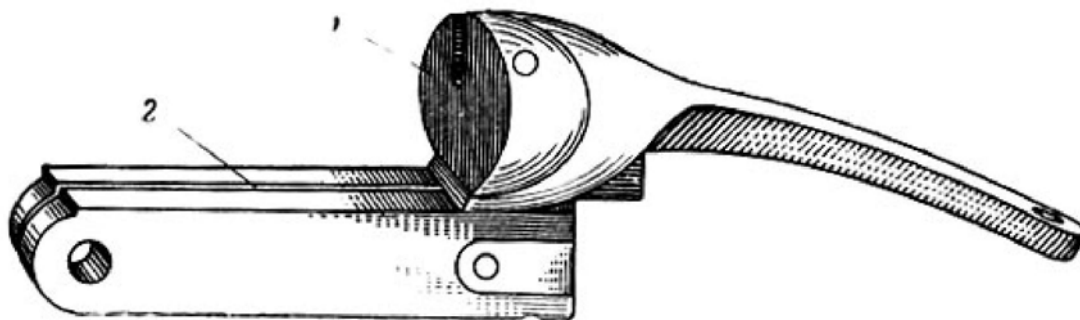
Коленчатая колодка: 1 - щиток; 2 - подушки
